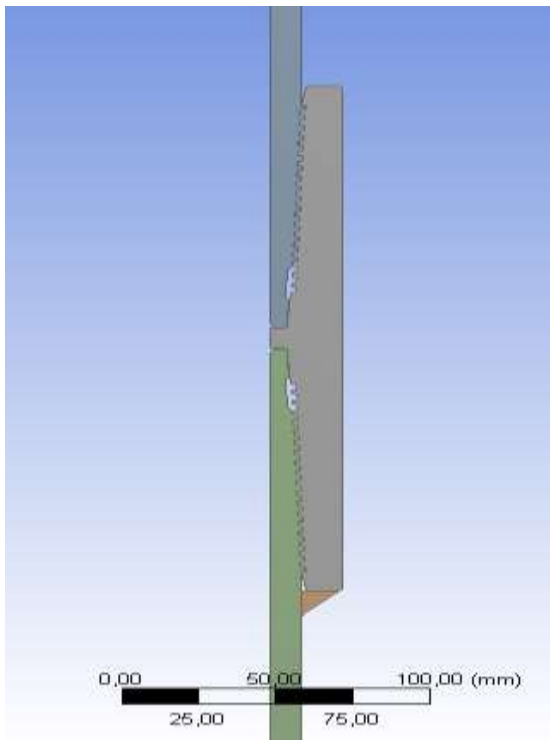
Геометрическая модель узла со сваркой.
